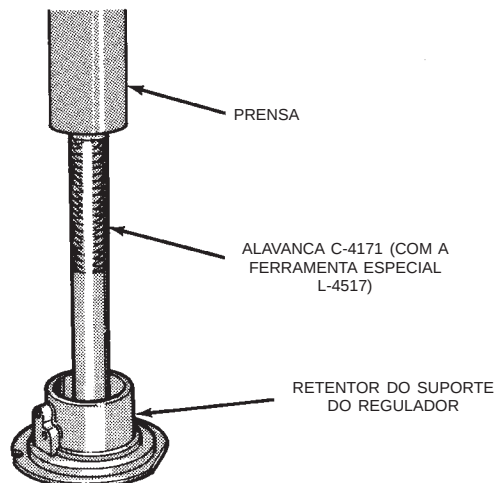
Remoção da Capa do Rolamento do Retentor do Suporte do Regulador
